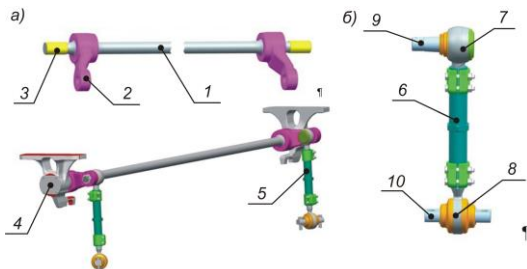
Элементы стабилизатора боковой качки:
